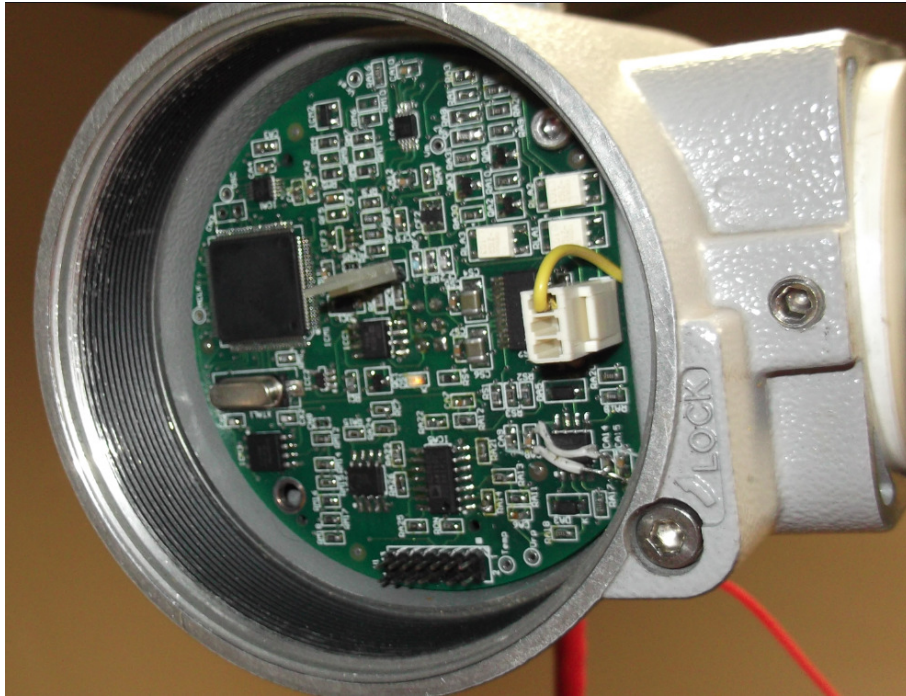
Placa eletrônica instalada no invólucro à prova de explosão
